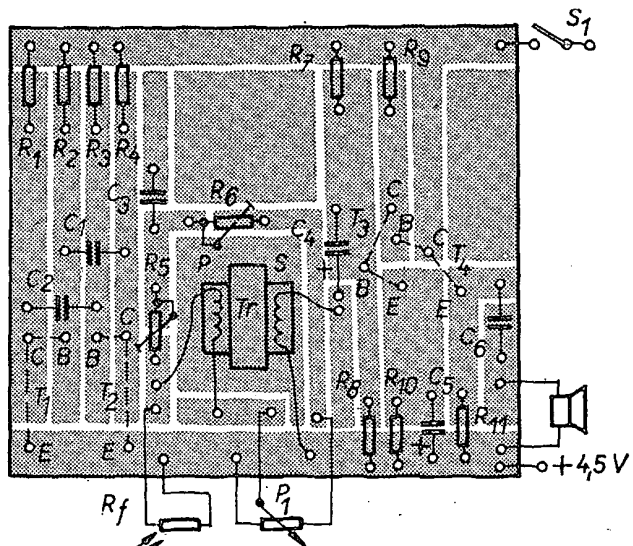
Destička s plošnými spoji pro zapojení z obr. 1 (Smaragd F01)
